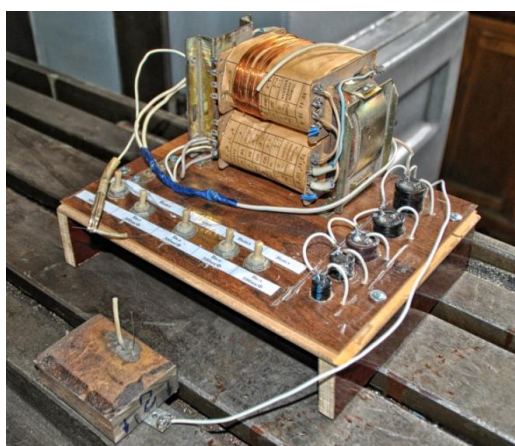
Пристрій конденсаторного зварювання для монтажу термопар
